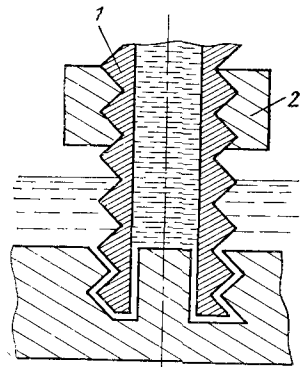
Образование винтовых отверстий электрод-инструментом, направляемым маточной гайкой
